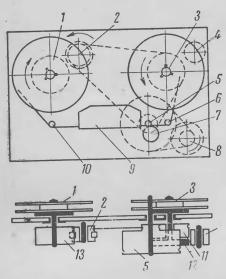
Қинематическая схема лентопротяжного механизма двухскоростного магнитофона.
